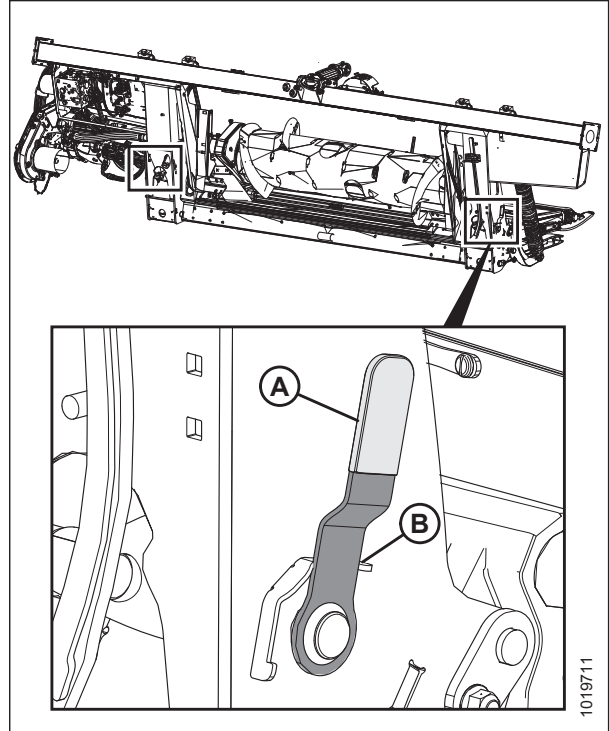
Manija de bloqueo de flotación: se muestra el lado derecho en detalle, opuesto al lado izquierdo
